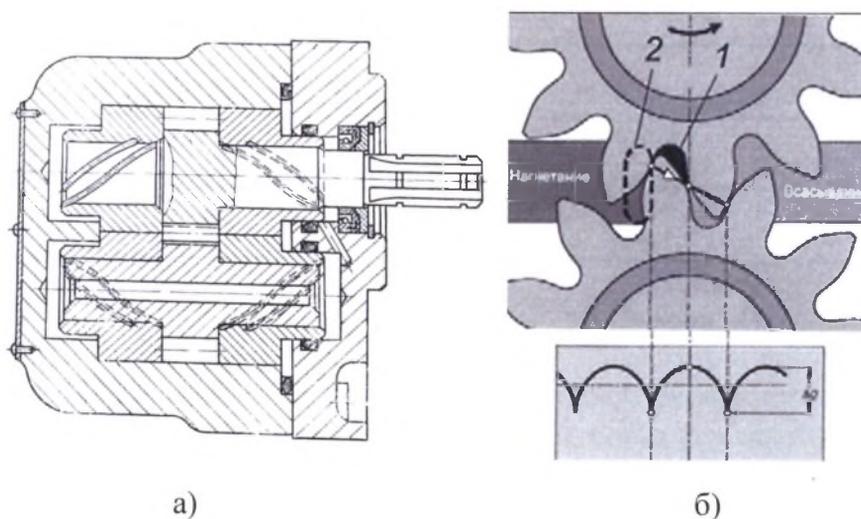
Шестеренный насос с шестернями наружного зацепления:
